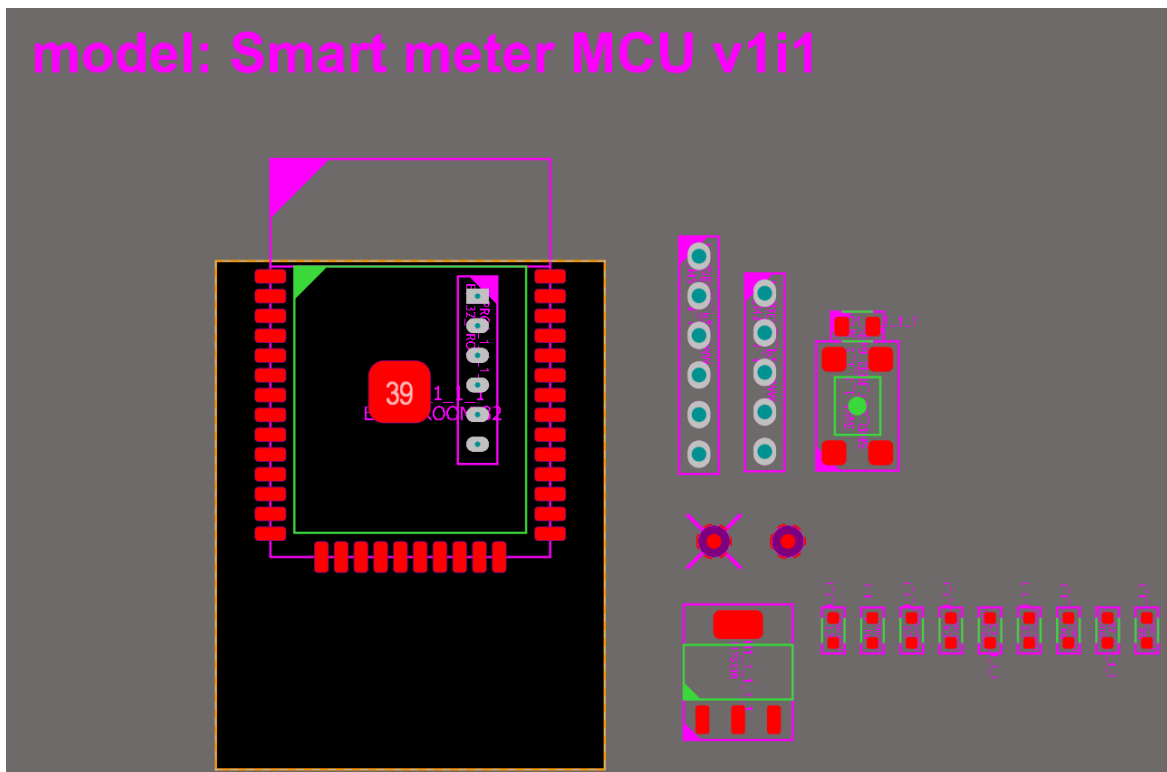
Σχεδίαση PCB - Περίμετρος ηλ.πλακέτας
